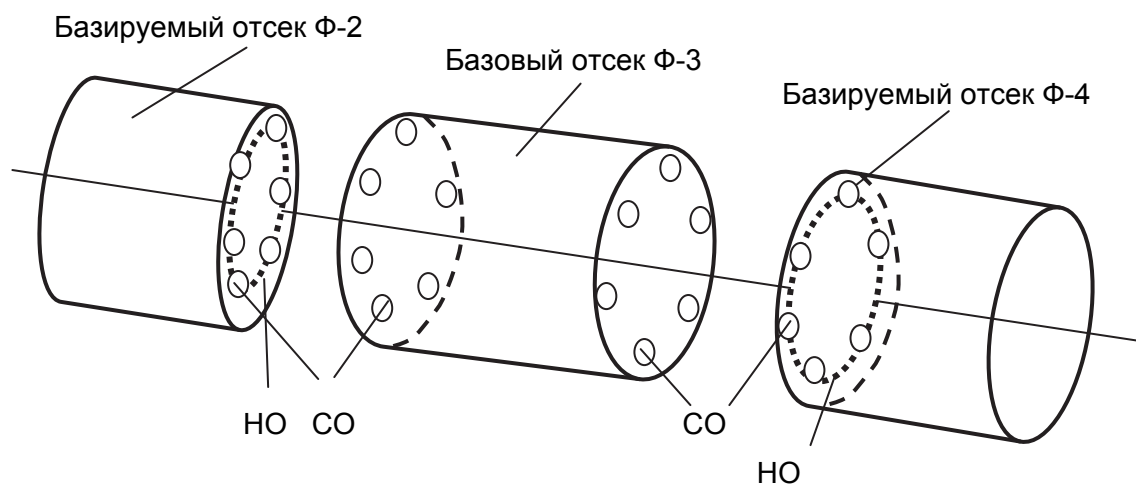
Схема стыковки отсеков фюзеляжа
